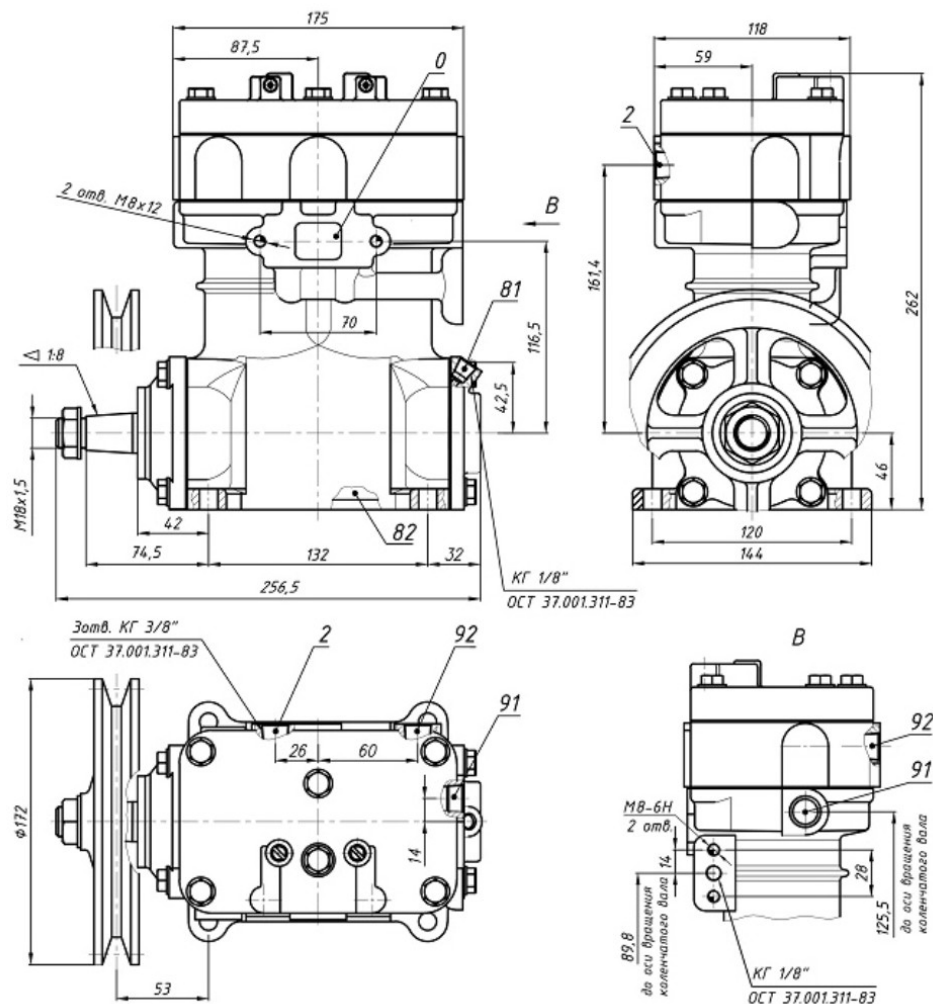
Присоединительные и установочные размеры компрессоров АМ.3509015-500-Б1.
